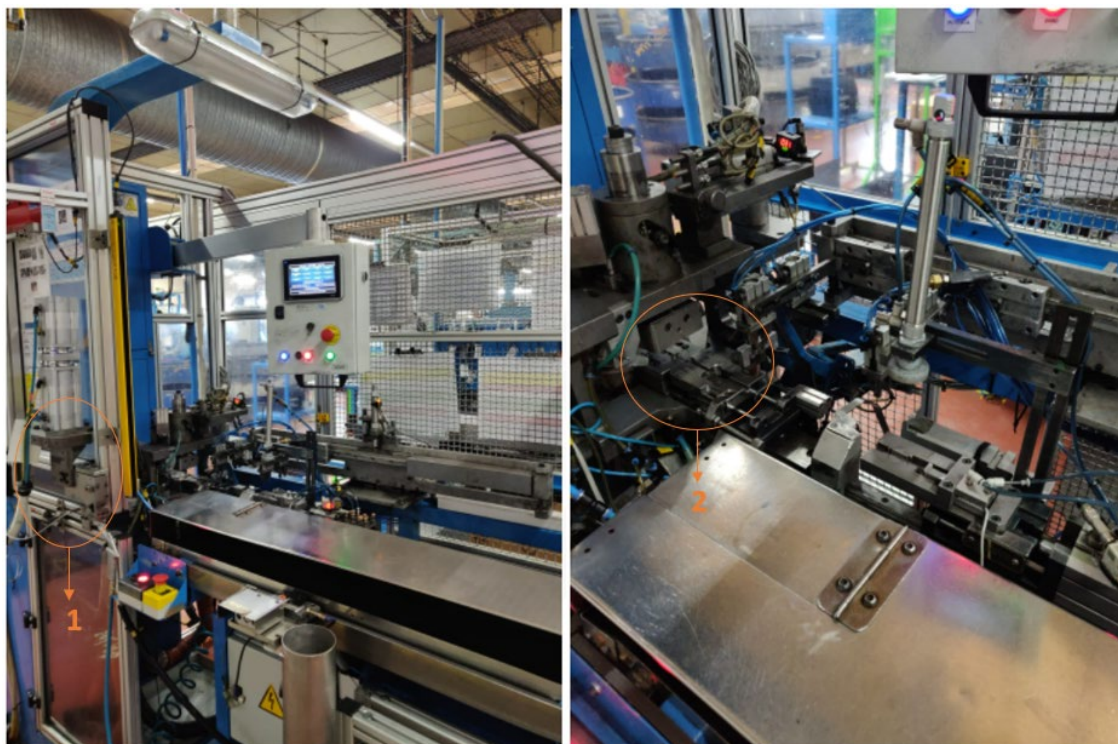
Posto de fazer flor e injetar 2º terminal de cabo; (1) – Dispositivo de fazer flor; (2) – Molde de injeção do 2º terminal de cabo
